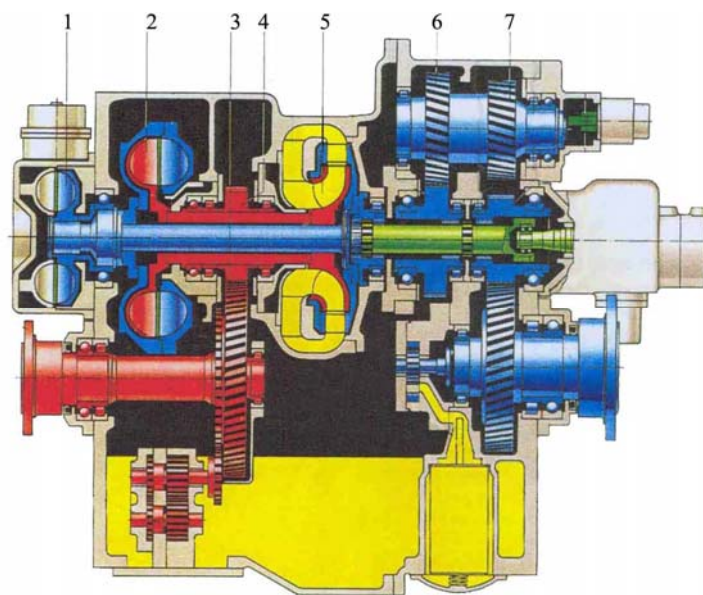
Конструкция турбопередачи фирмы «Фойт»: 1 – гидродинамический тормоз; 2 – гидромуфта; 3 – входной вал; 4 – ведомый вал; 5 – гидротрансформатор; 6 – привод переднего хода; 7 – реверсивное устройство
